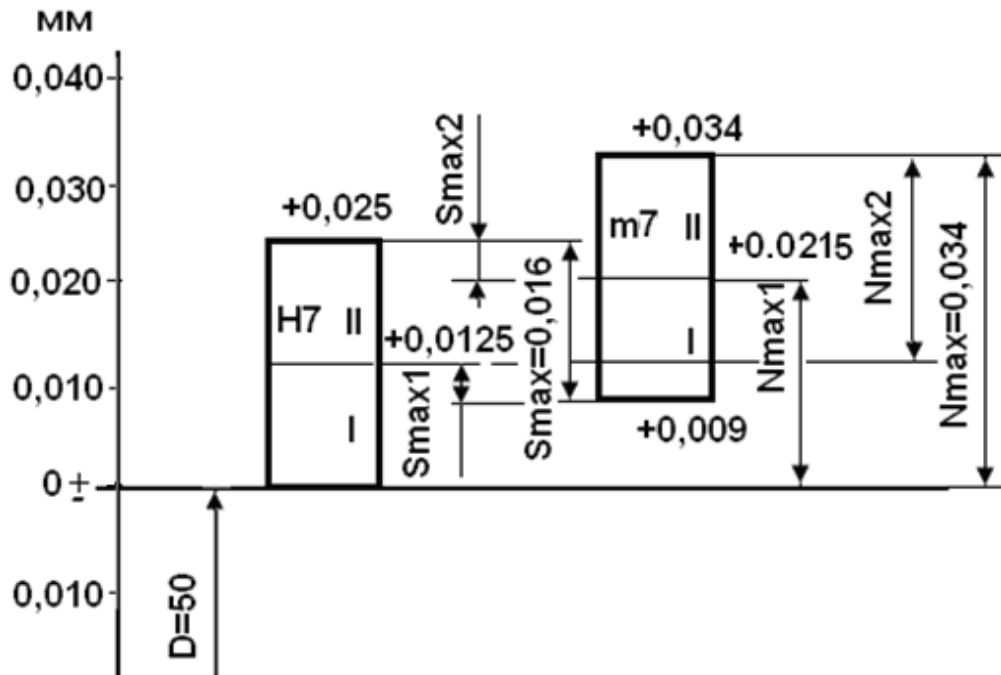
Схема розташування полів допусків з'єднання $\varnothing 50H7/m7$
